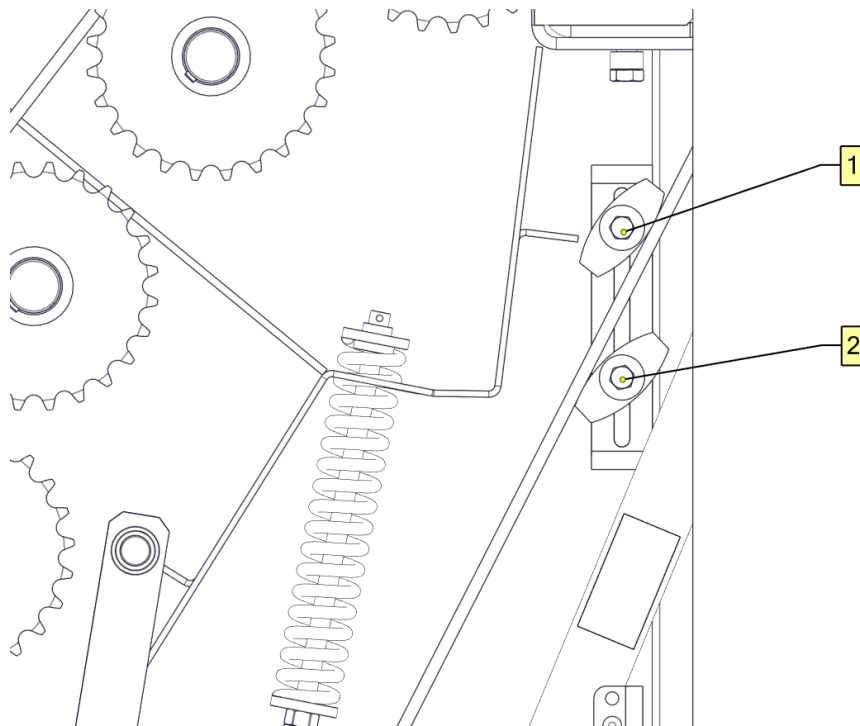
Регулировка проведения цепи с левой стороны пресс-подборщика
